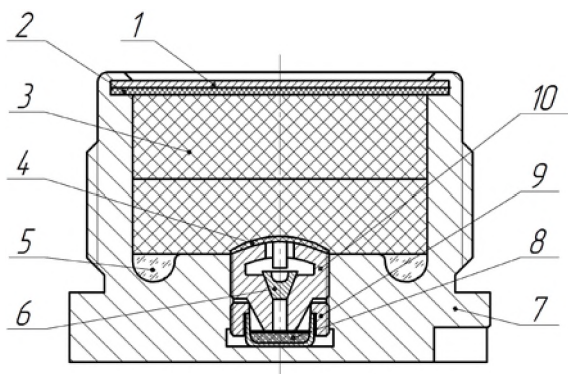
Капсюльная втулка КВ-4: 1 – латунный кружок; 2 – пергаментный кружок; 3 – пороховые петарды; 4 – бумажный кружок; 5 – подсыпка из дымного пороха; 6 – обтюрирующий конус; 7 – корпус; 8 – капсюль-воспламенитель; 9 – прижимная втулка; 10 – наковаленка
